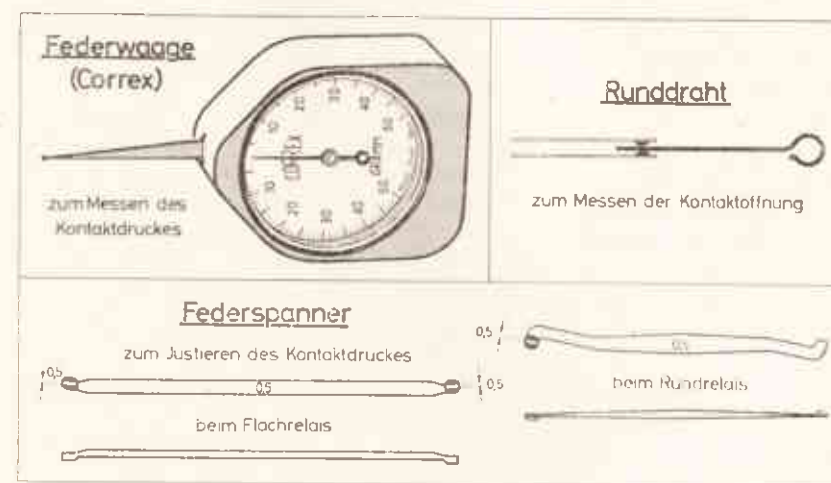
Einstell-(Justier-)Werkzeuge für Relaiskontakte
